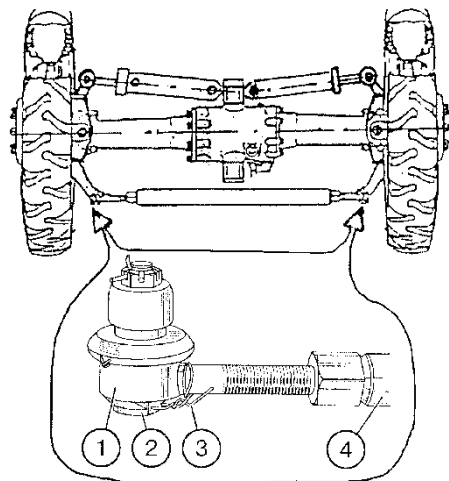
Проверка люфта в шарнирах рулевой тяги: 1 – шарнир; 2 – резьбовая пробка; 3 – контровочная проволока; 4 – рулевая тяга
